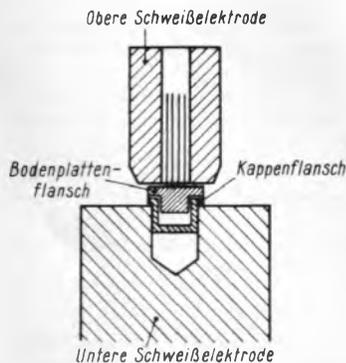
Die Elektroden der Ringschweißmaschine in Schweißstellung (schematische Darstellung)
